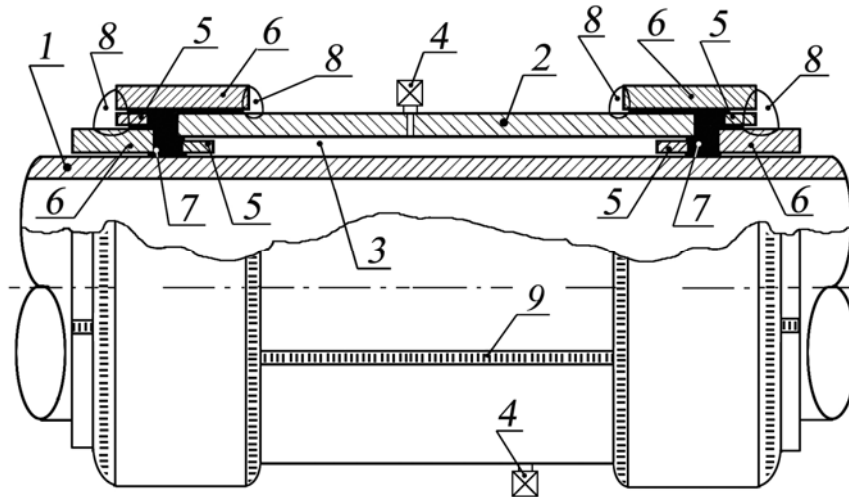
Конструкции наиболее распространённой клеево-сварной муфты без приваркой к телу трубы, где: 1 – трубопровод, 2 – муфта, 3 – подмуфтовое пространство, 4 – штуцеры, 5 – сварочная лента, 6 – технологические кольца, 7 - торцевые уплотнители, 8 – кольцевые сварные швы, 9 – продольные сварные швы
